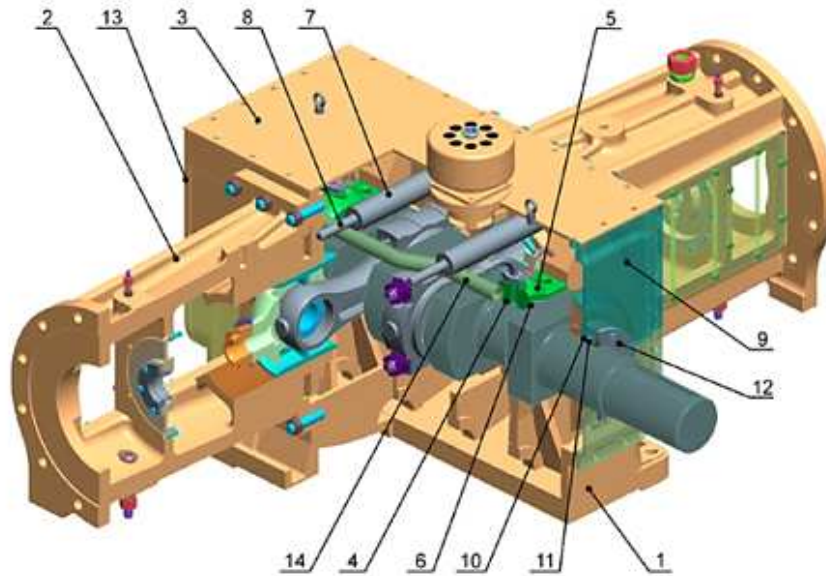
Оппозитная база 2М10А быстроходного компрессора 2ГМ10А-2,7/21-151: 1 – картер; 2 – направляющая; 3 – крышка картера верхняя; 3 – вкладыш; 4 – крышка подшипника; 6 – полукольцо; 7 – распорка; 8 – стяжка; 9 – крышка маслоснимателя; 10 – манжета; 11 – кольцо; 12 – фланец; 13 – крышка картера передняя; 14 – коллектор смазки коренных подшипников.
